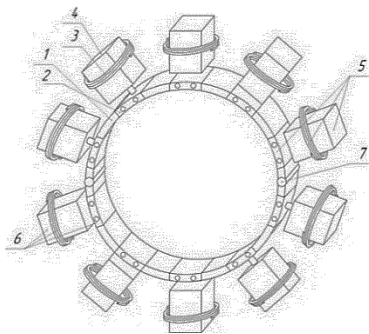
Электромагнитно-акустический преобразователь для контроля объектов цилиндрической формы:
